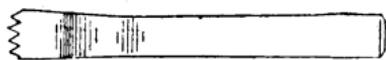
Outil à fileter, pas jusqu'à 3 millim.
